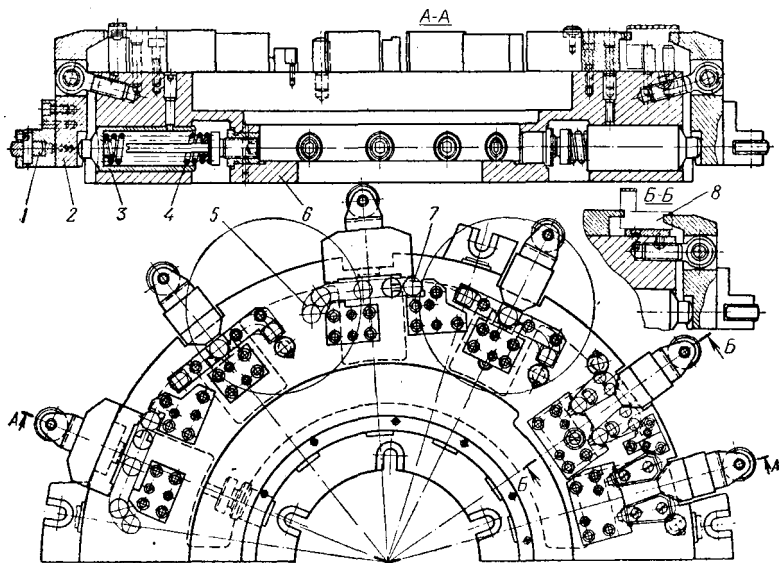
Приспособление для непрерывной обработки плоскостей рычагов
